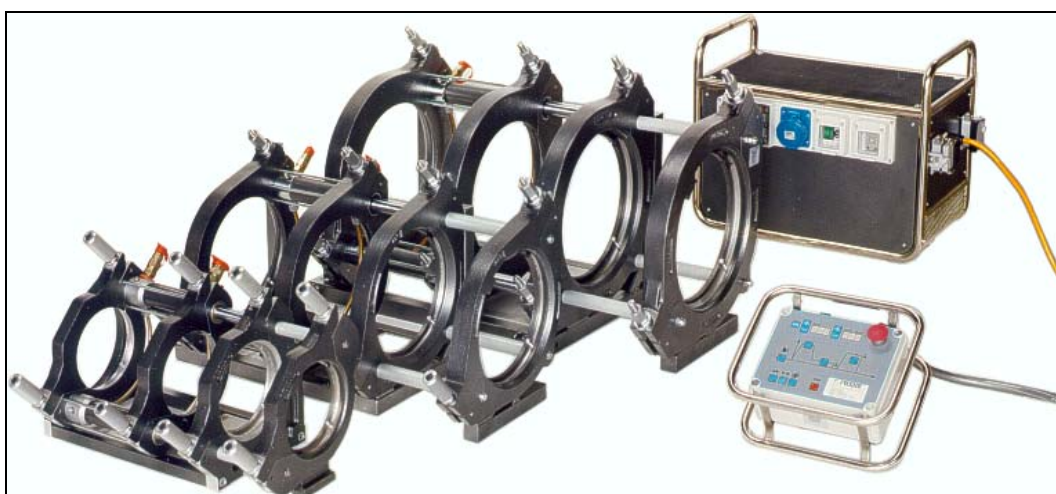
Heizelementstumpfschweißmaschine für den Baustelleneinsatz
